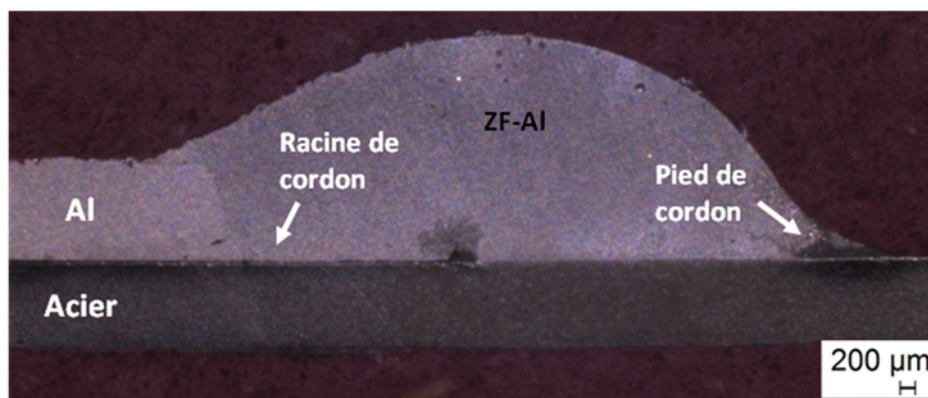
Coupe transversale d'un assemblage acier/aluminium à clin (essai 5).
